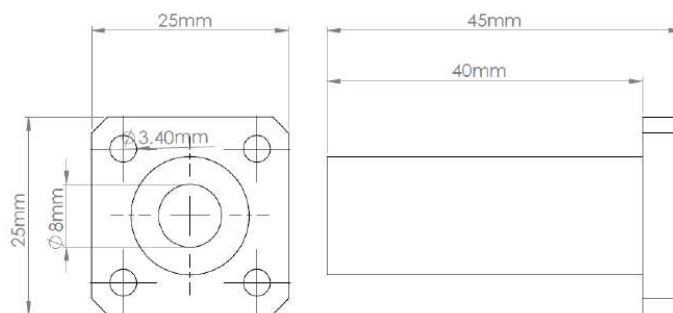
Dimensiones del rodamiento lineal para los soportes del estator [8].
